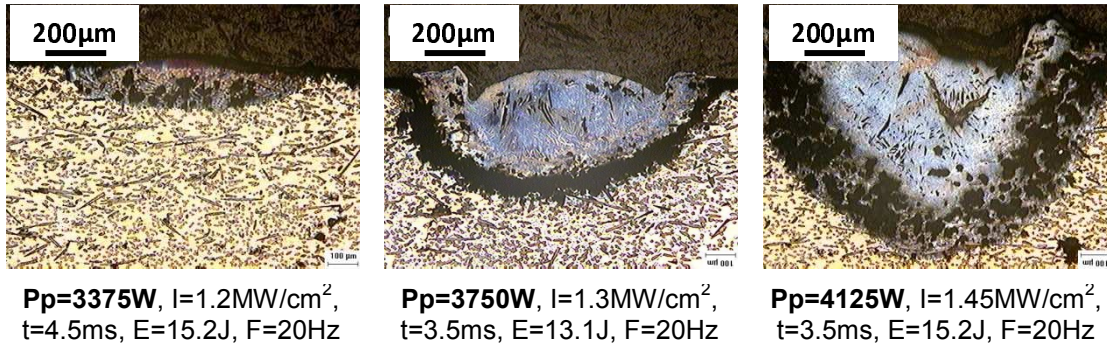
Efecto de los parámetros de soldadura sobre la profundidad y ancho del cordón.
